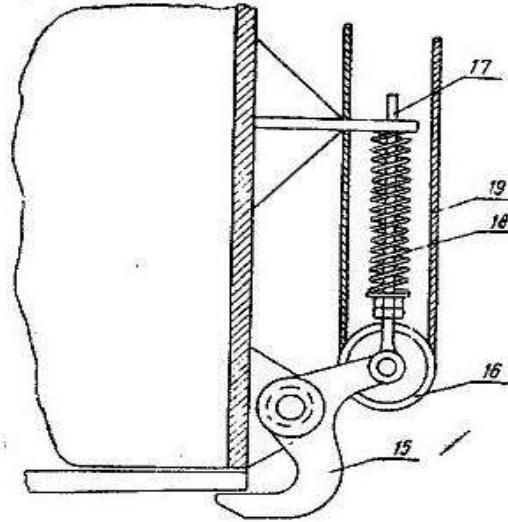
Вид збоку механізму відкривання днища ковша [10]
